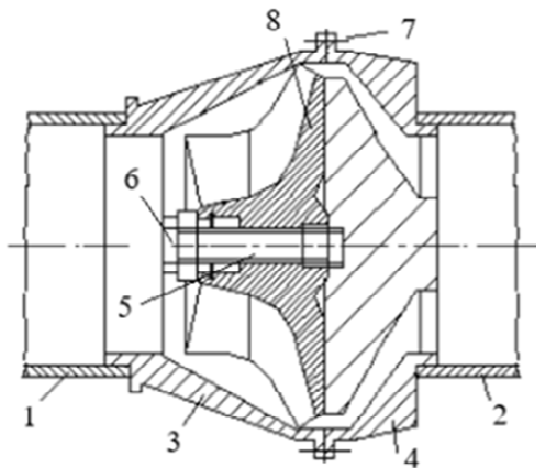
Общая схема базирования и закрепления заготовки в приспособление для обработки абразивным потоком: 1 - верхний рабочий цилиндр; 2 - нижний рабочий цилиндр; 3 - крышка; 4 - основа приспособления; 5 - резьбовые шпильки; 6 - крепежная гайка; 7 - соединительные болты; 8 - обрабатываемая деталь.
